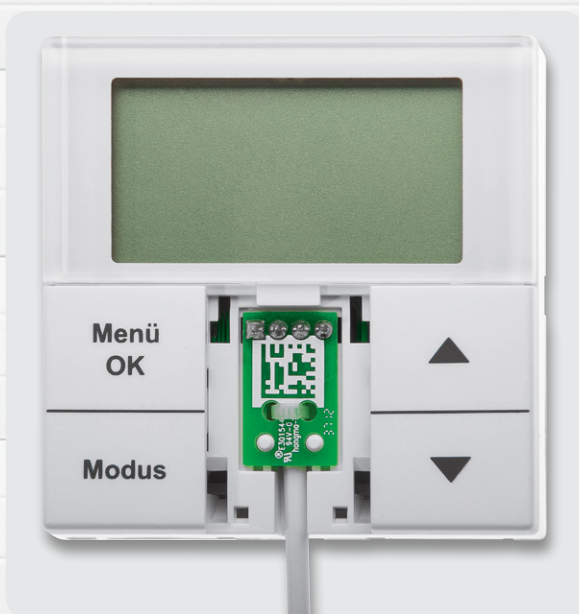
Jetzt wird die Steckerplatine eingesetzt und abschließend die Gehäuseabdeckung wieder aufgesetzt.
